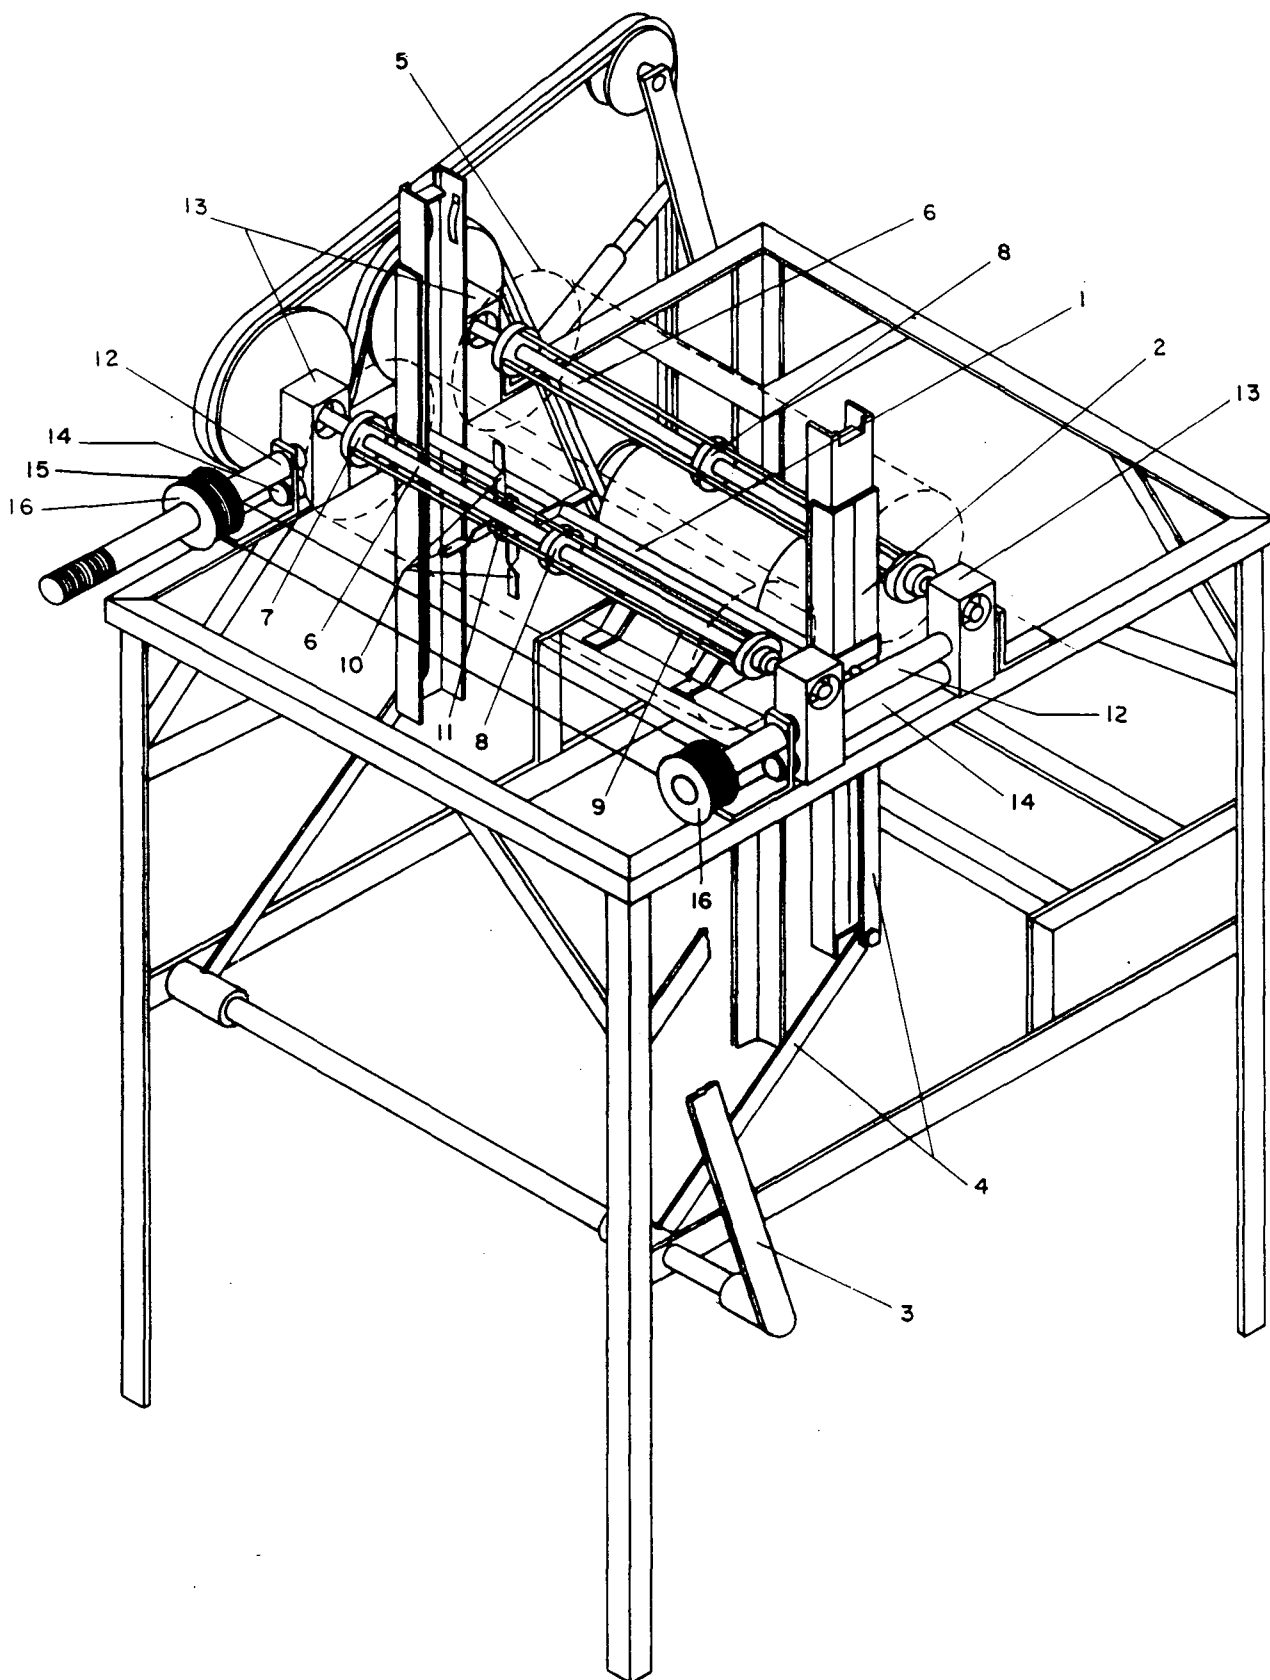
Desenho em perspectiva da máquina desoperculadora.
